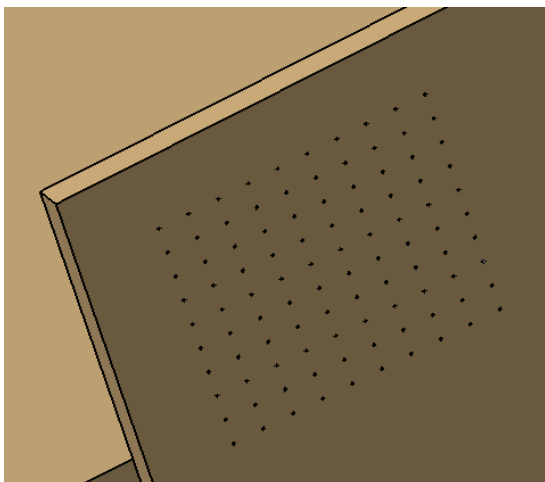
Detalle filtro 2. Diámetro 1 mm.
